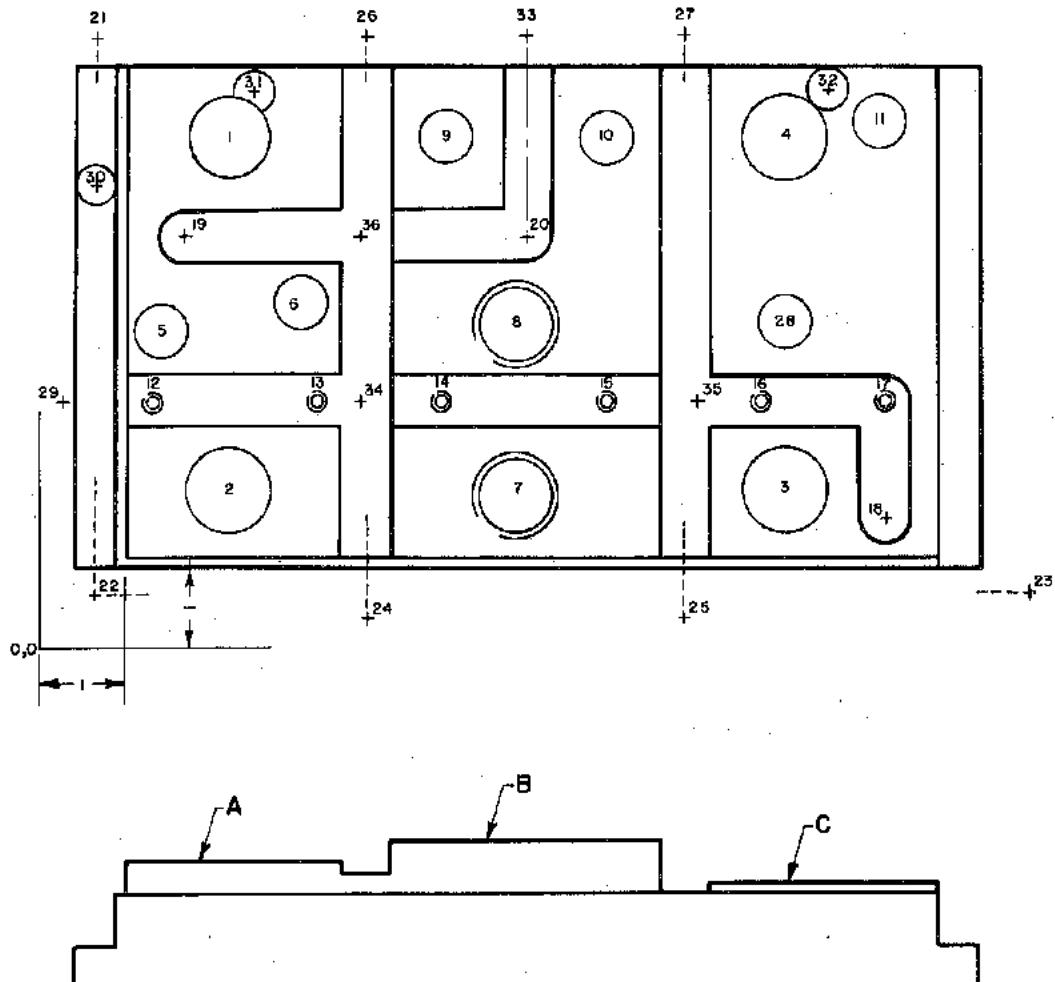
Dibujo del mismo banco de pruebas adaptado para un programa numérico (Cincinnati Milling Machine Co.)
